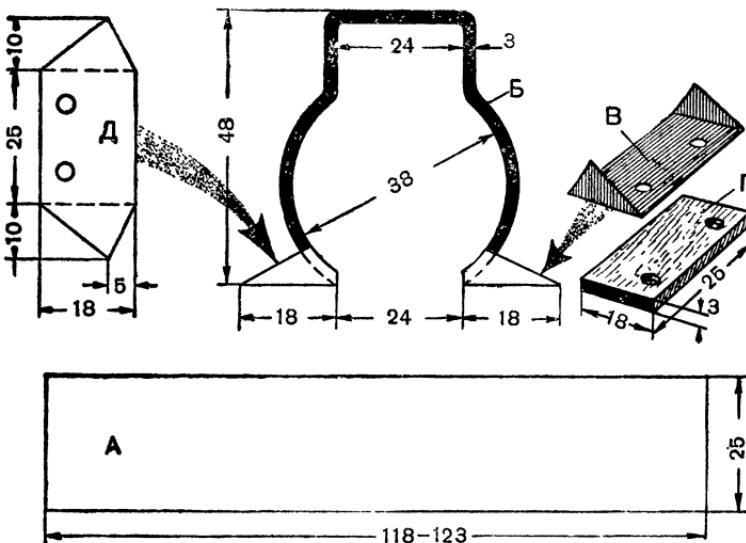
Детали статора № 2 (рис. 12): А — полоска жести; Б — пакет изогните так; В — скоба; Г — прокладка; Д — заготовка для скобы.
